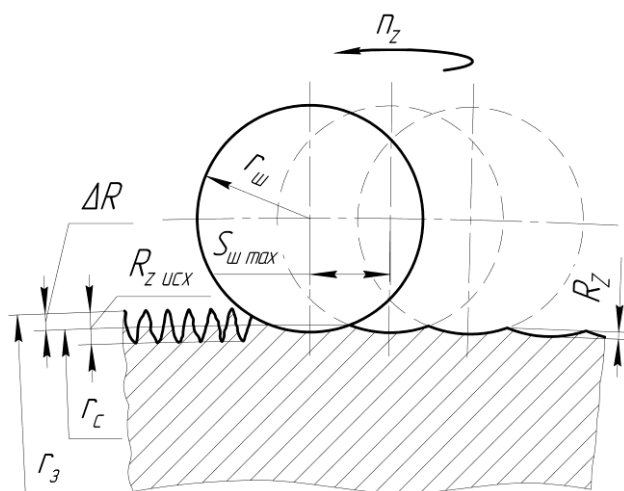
Схема отделочно-упрочняющей обкатки сферической поверхности
